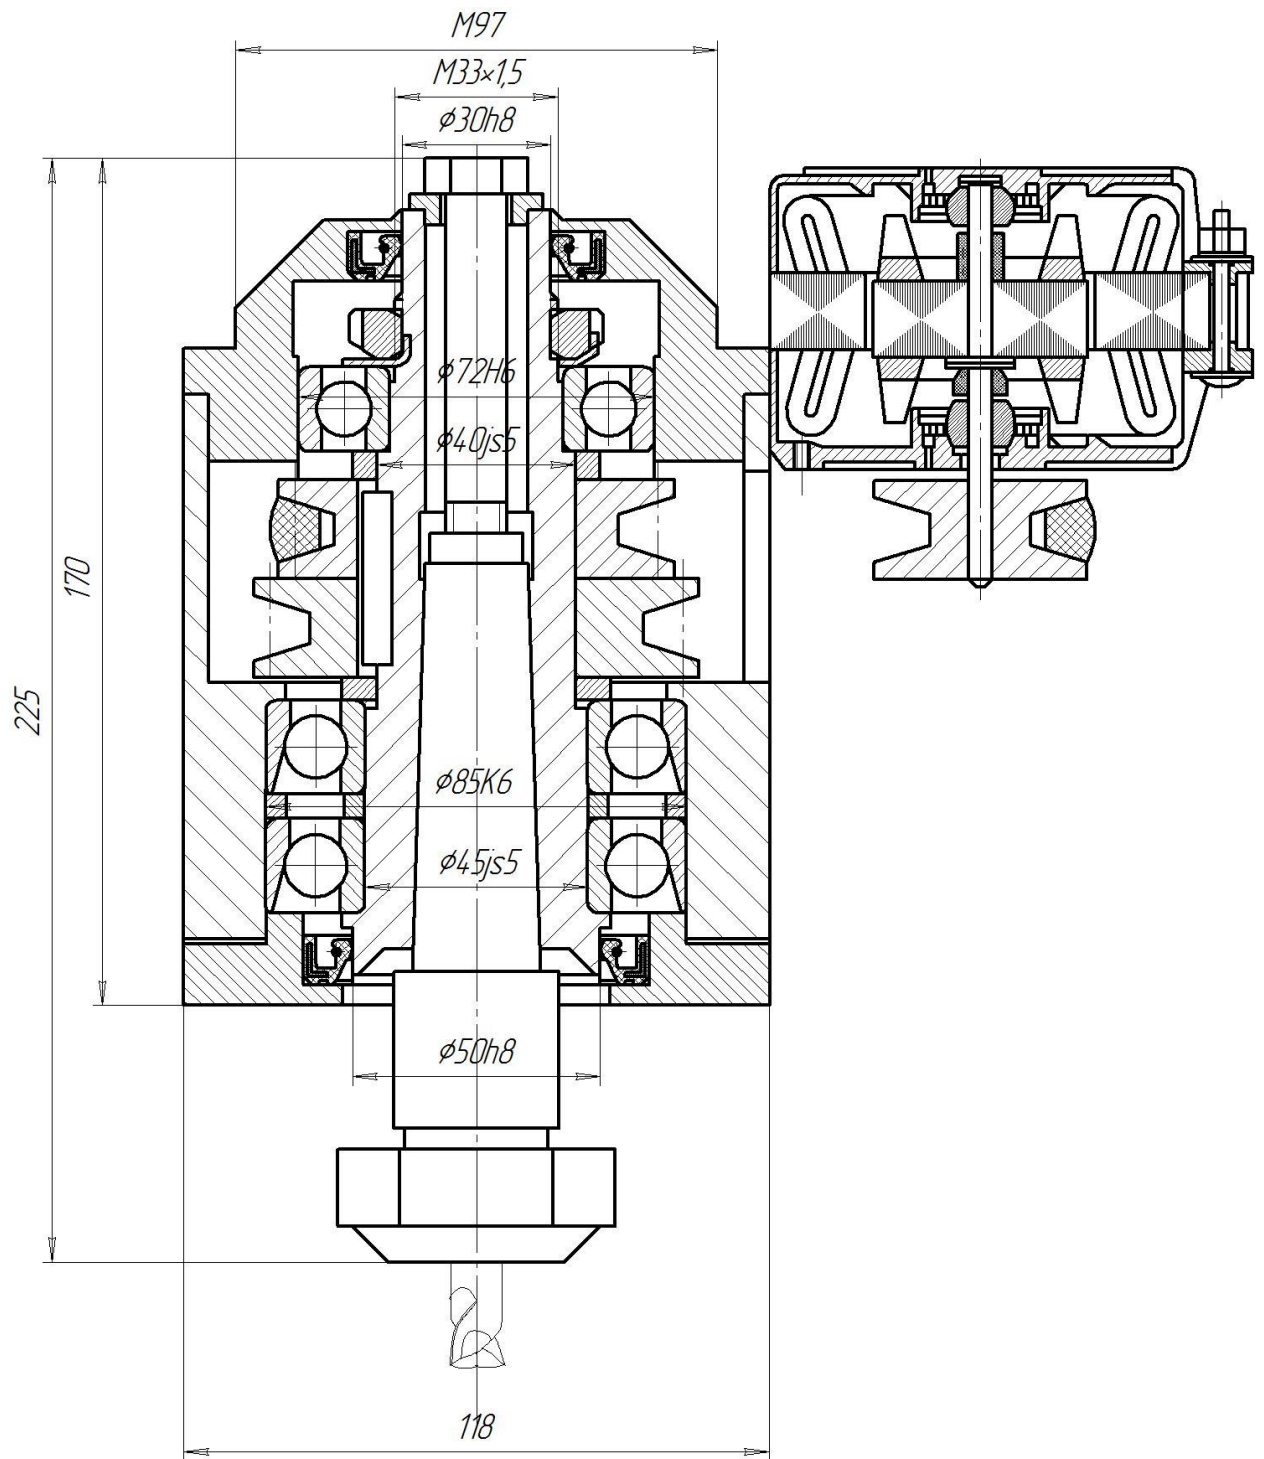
Конструкція шпиндельного вузла з пасовою передачею.
